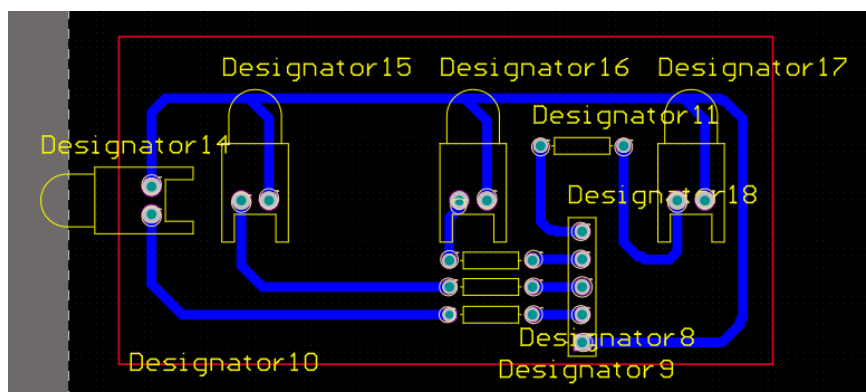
Primer diseño de placa PCB mediante el programa Altium
